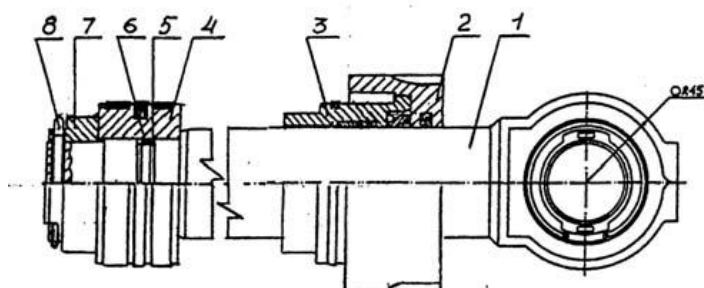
Шток в сборе: 1 – шток; 2 – гайка в сборе; 3 – втулка в сборе;
